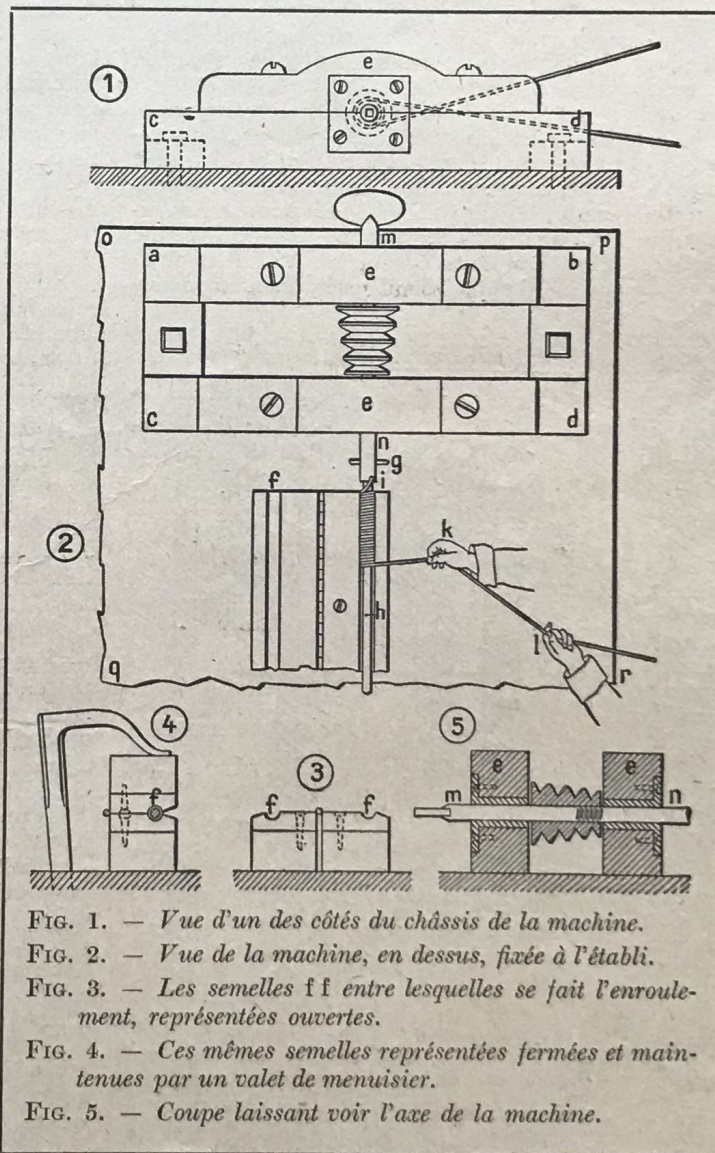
Vue d'un des côtés du châssis de la machine.
